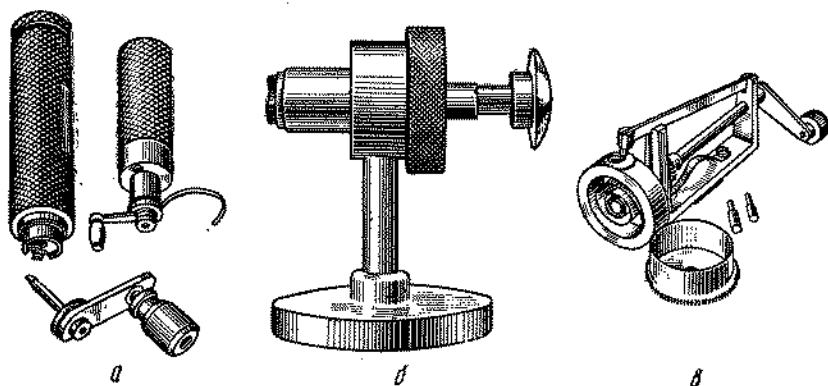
Приспособления для навивки и вставки пружины в барабан:
